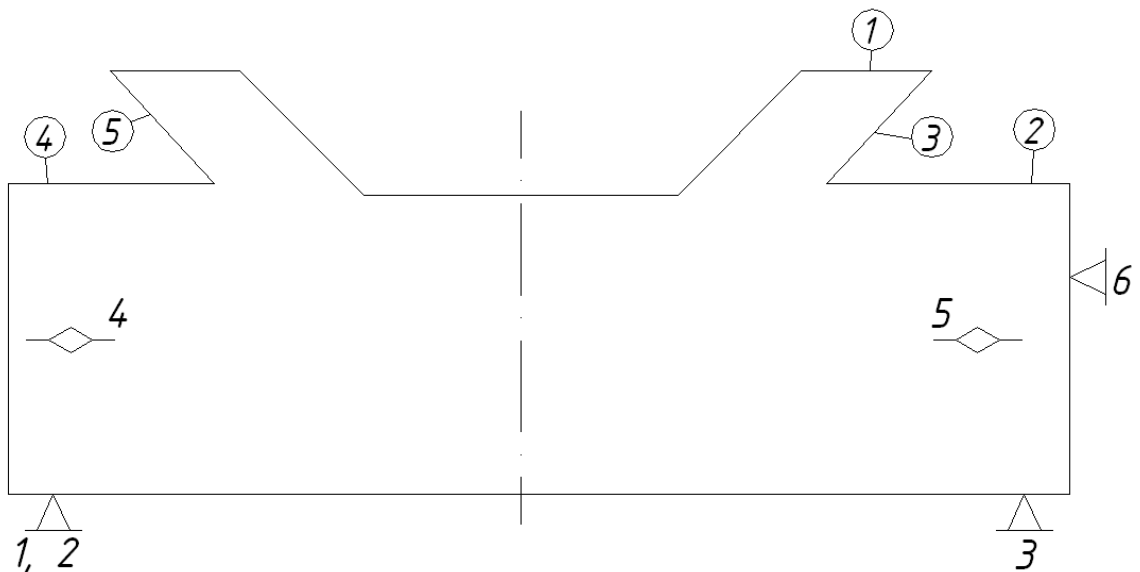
Теоретична схема базування при обробці чорнових баз
